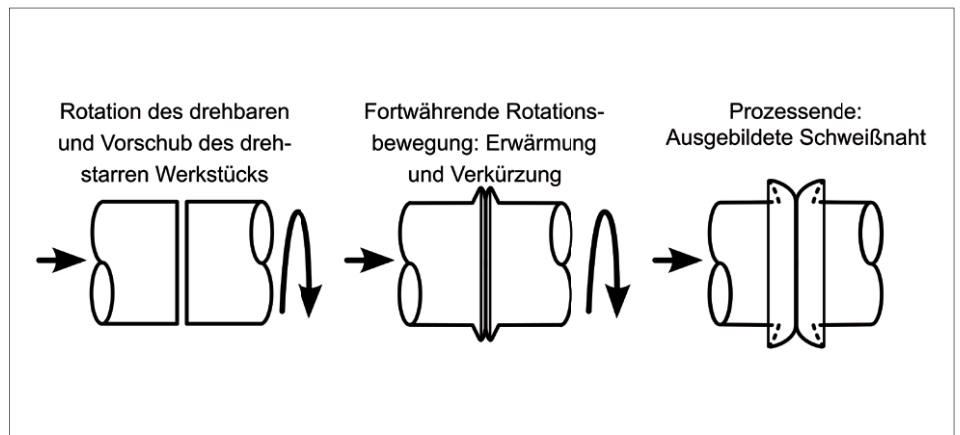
Prinzipieller Verfahrensablauf beim Rotationsreibschweißen
